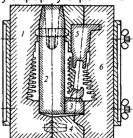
Формовка в стержнях цилиндра двигателя с воздушным охлаждением
